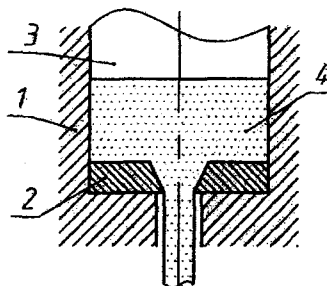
Мундштучное формование: 1 – контейнер; 2 – матрица; 3 – пуансон; 4 – порошковая заготовка
